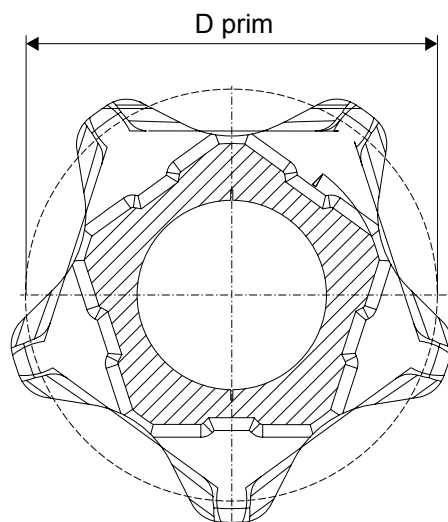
Dimensions de la noix ; SL05-SL10, SR25
